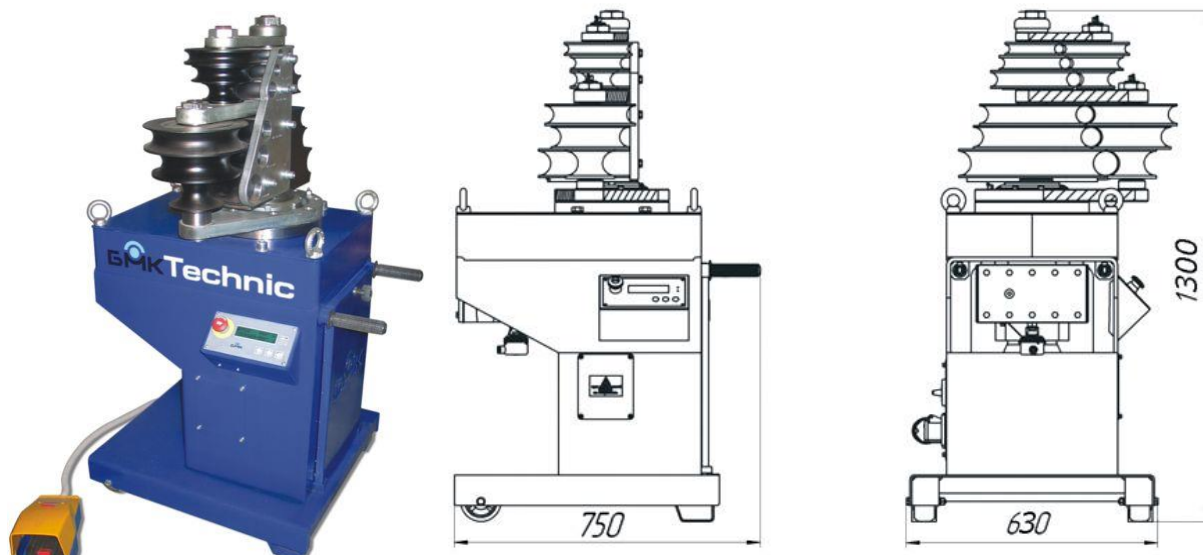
Общий вид и схема модели станка RE-60
